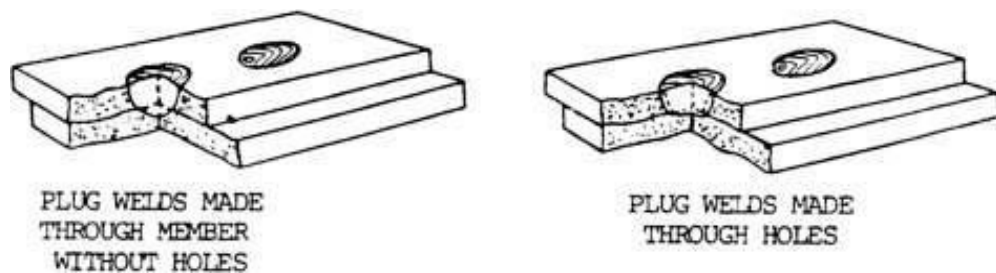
Esquema de una soldadura de tapón y ranura.
